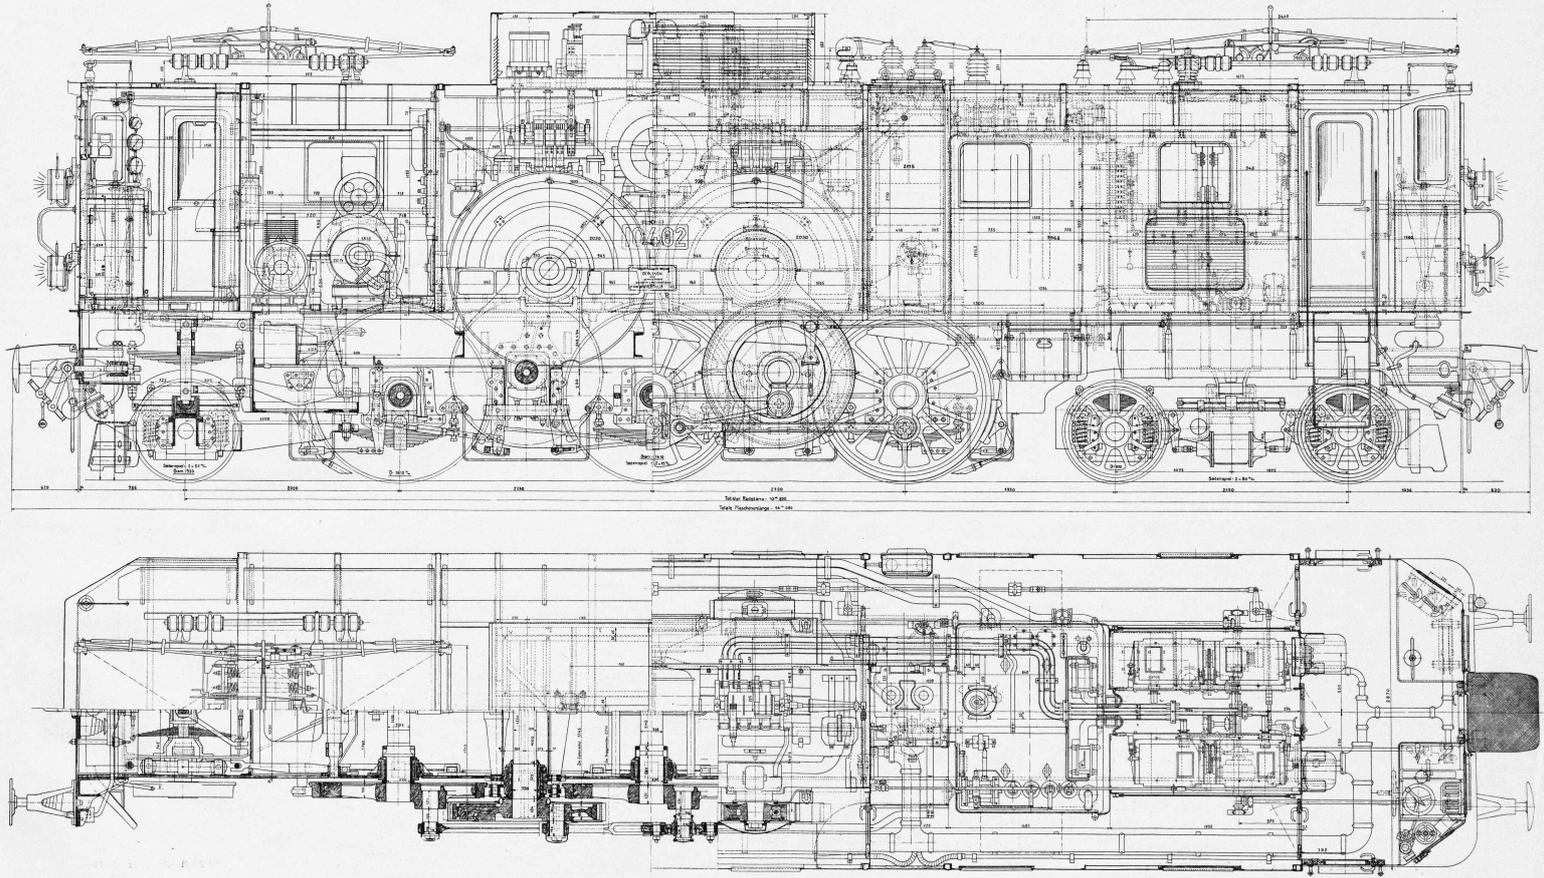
und 3. Längsschnitt und Ansicht, Draufsicht und Horizontalschnitte. — Masstab 1:35.
